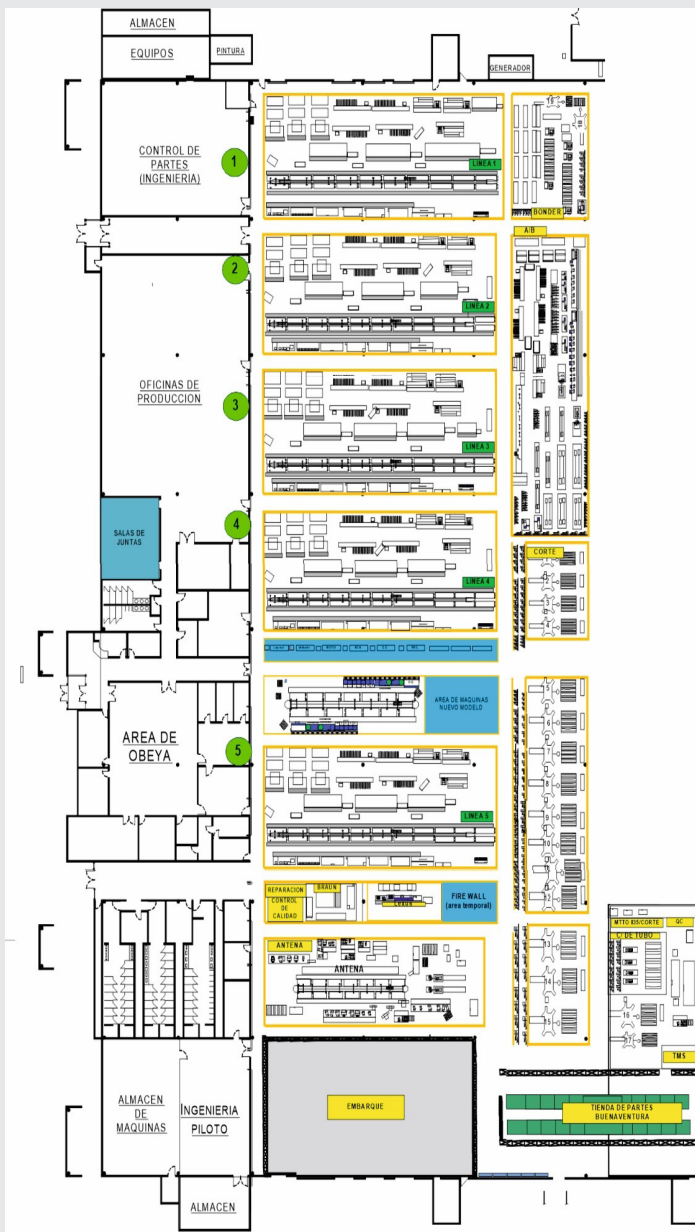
Plano de Planta Buenaventura Autopartes S.A de C.V.
